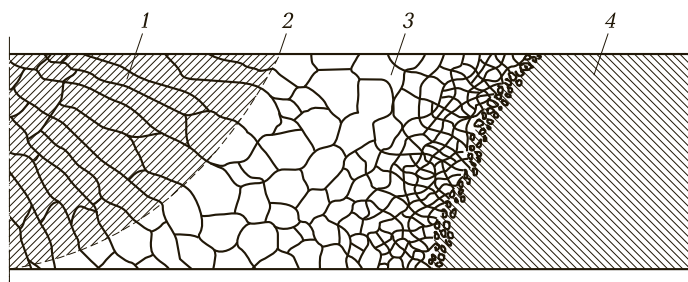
Основные структурные зоны в поперечном сечении сварного соединения:
